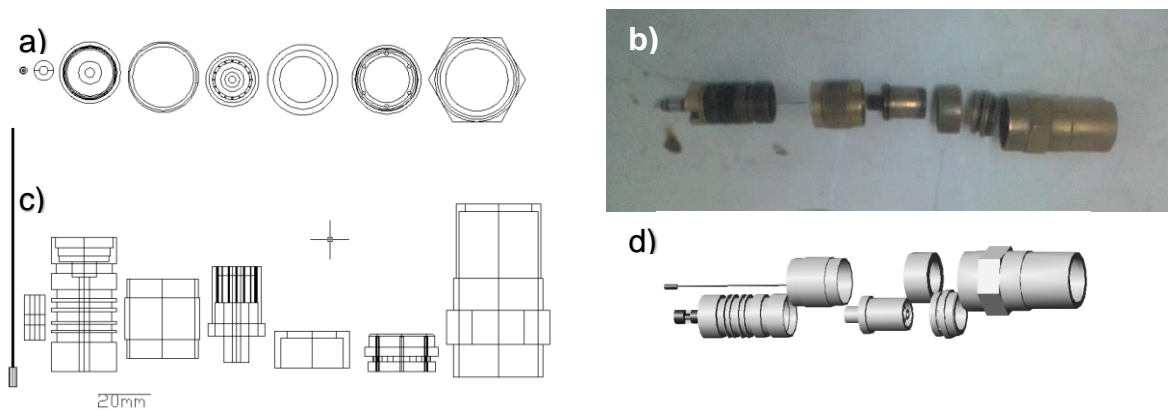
Distribución de piezas que componen la boquilla a) vista frontal, b) fotografía de la boquilla, c) vista lateral, d) Ensamble de la boquilla. [22]
